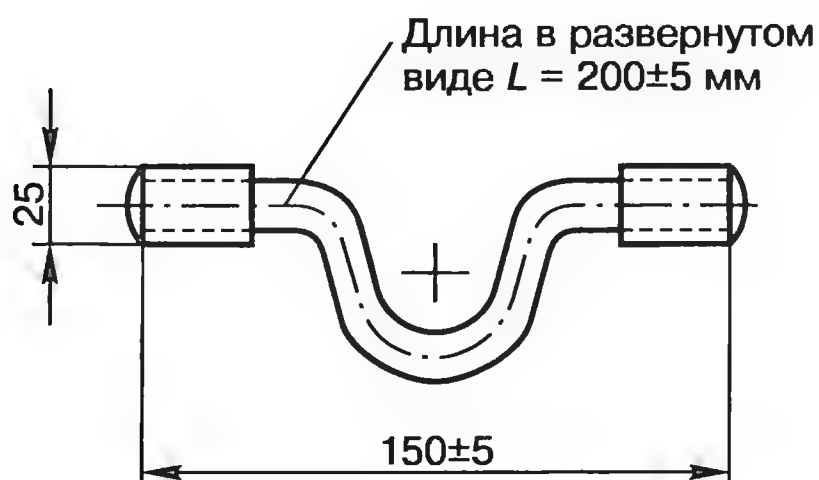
Соединитель рельсовый стыковой медный приварной типа Щ67-00-00
